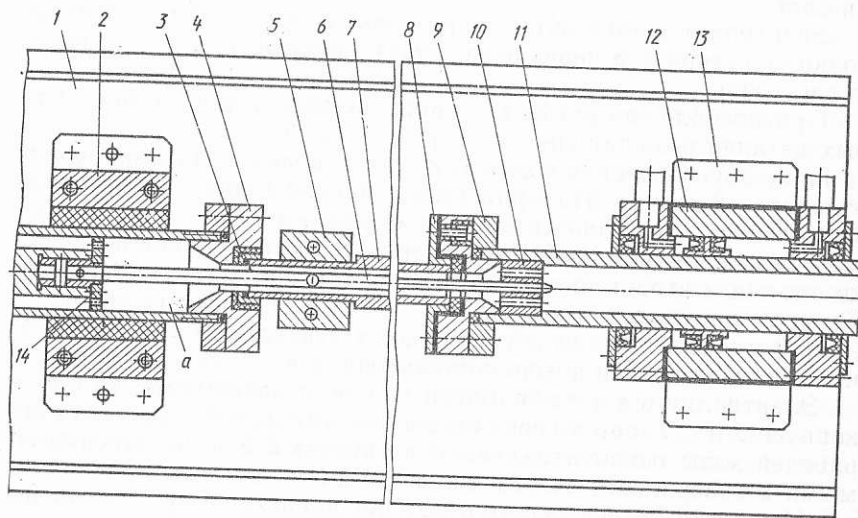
Приспособление для ЭХО отверстий неподвижным ЭИ
